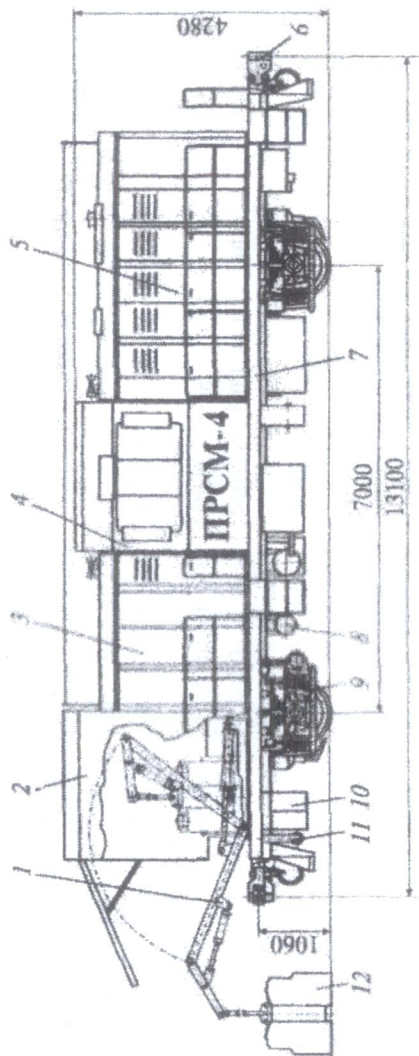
Путевая рельсосварочная машина ПРСМ-4: 1 — гидравлический манипулятор; 2 — подъемный капот с торцевой стенкой; 3 — отсек для размещения оборудования подвесной сварочной машины, гидроаппаратуры и электроаппаратуры; 4 — кабина управления; 5 — дизель-электрическая установка; 6 — автосцепка; 7 — рама; 8 — тормозная система; 9 — приводная колесная пара; 10 — инструментальный ящик; 11 — подтягивающее устройство; 12 — подвесная сварочная головка
